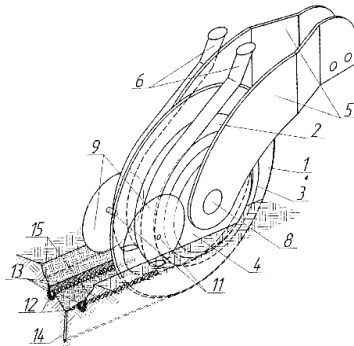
Технологическая схема работы комбинированного однодискового сошника с двусторонними ребордами и дисковыми загортачами для узкорядного посева: 1 – плоский диск; 2 – внутренняя реборда; 3 – бороздкообразователь; 4 – наружная реборда; 5 – корпус; 6 – семянаправители; 8 – ось; 9 – сферические диски; 11 – ось; 12 – ложе; 13 – семена; 14 – щель; 15 – бороздки
